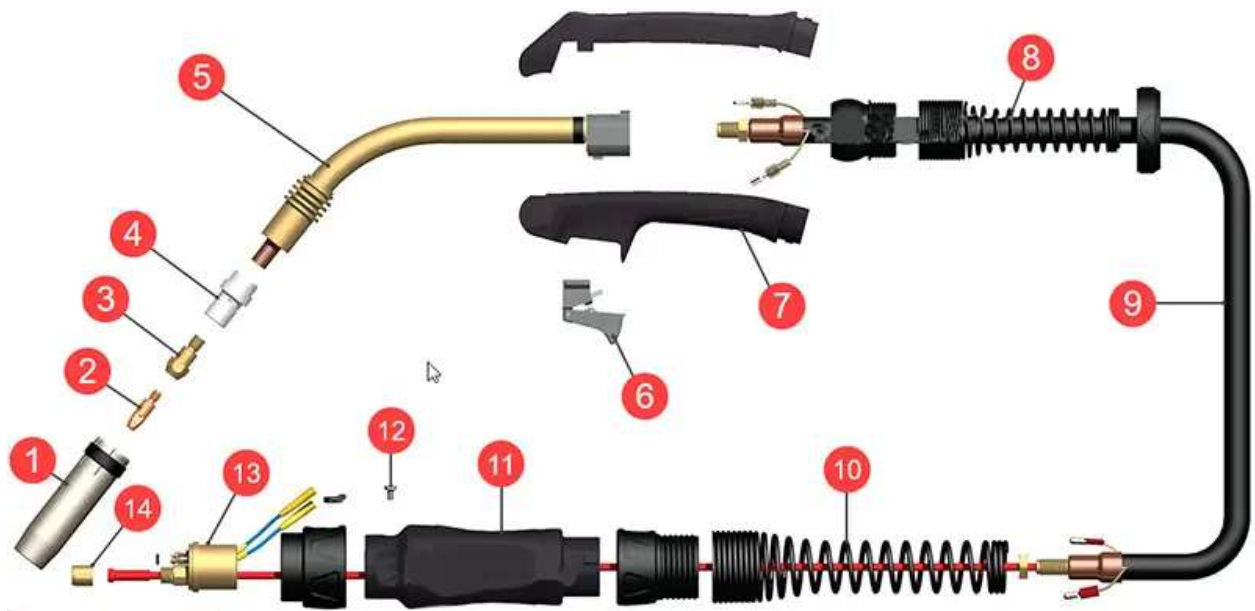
Пальник для MIG/MAG зварювання
